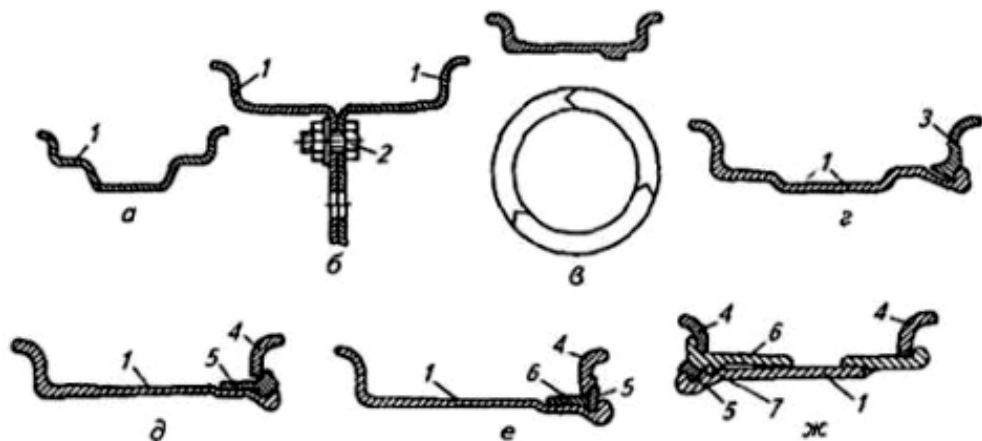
Основные типы ободьев колес: а - неразъёмный глубокий симметричный; б - разъёмный посередине; в - сегментный типа "триллекс", разделенный по радиусу на три сегмента; г - разъёмный двухкомпонентный; д - разъёмный трехкомпонентный; е - четырёхкомпонентный; ж - пятикомпонентный; 1 - основание обода; 2 - соединительный элемент; 3 - разъёмное бортовое кольца; 4 - бортовое кольцо; 5 - пружинное замочное кольцо; б - посадочное кольцо; 7 - уплотнитель под бескамерную шину
